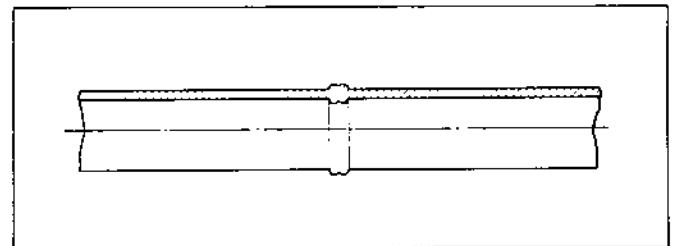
Saldatura testa a testa con tubi di PE a.d.
